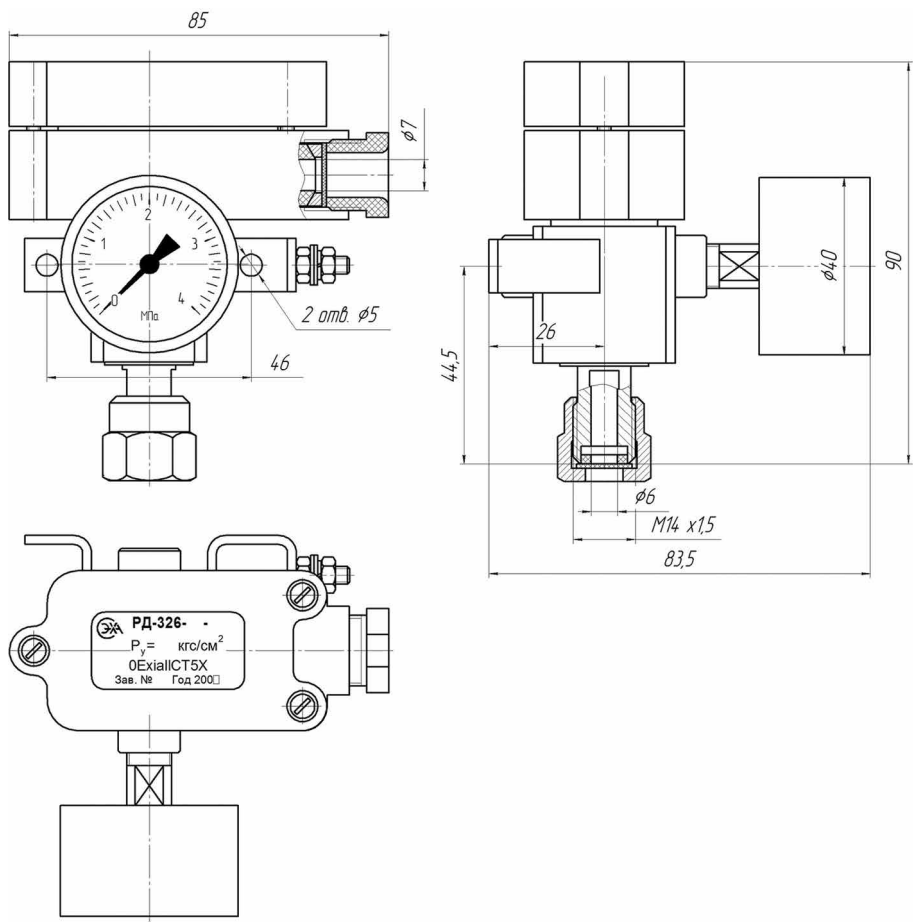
Габаритные и установочные размеры реле давления РД-326
